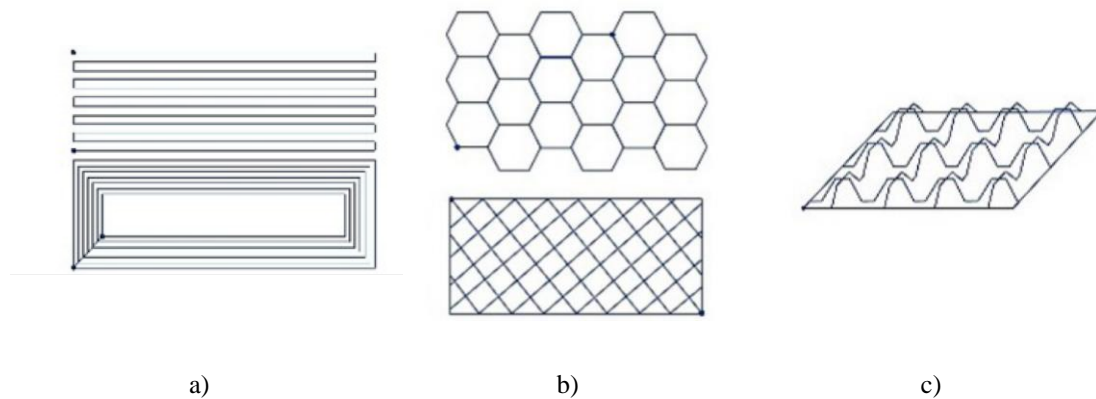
Patrones de impresión cFF; en plano a) sin fibras entrelazadas, b) con fibras entrelazadas y c) fuera de plano [LiN2020].
